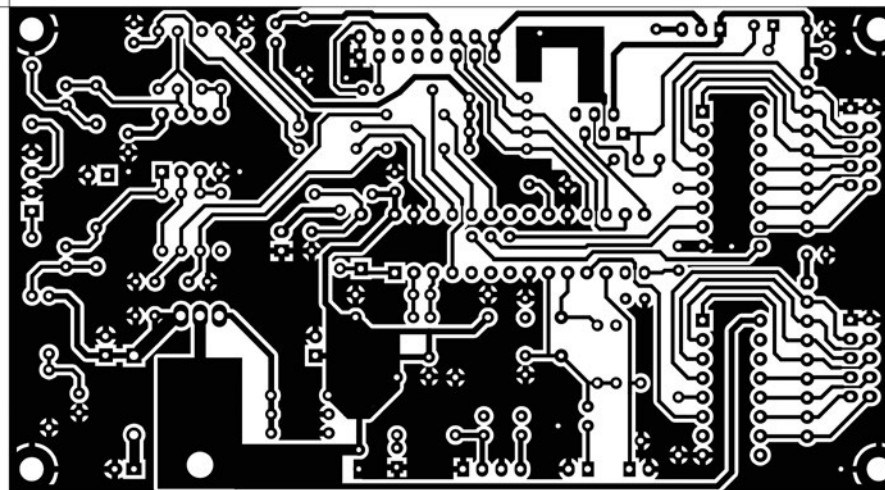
• Master in bianco/nero del lato BOTTOM (visto in trasparenza) del PCB in scala 1:1
